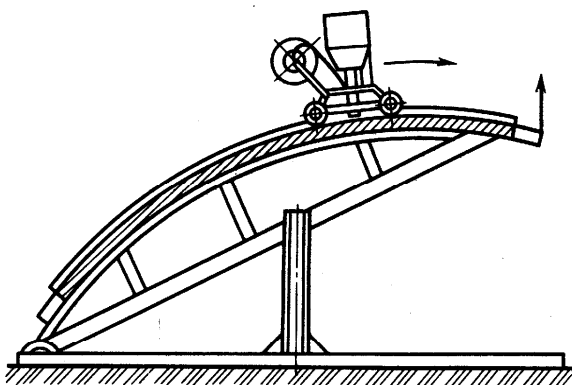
Стенд для автоматической дуговой сварки швов блока
